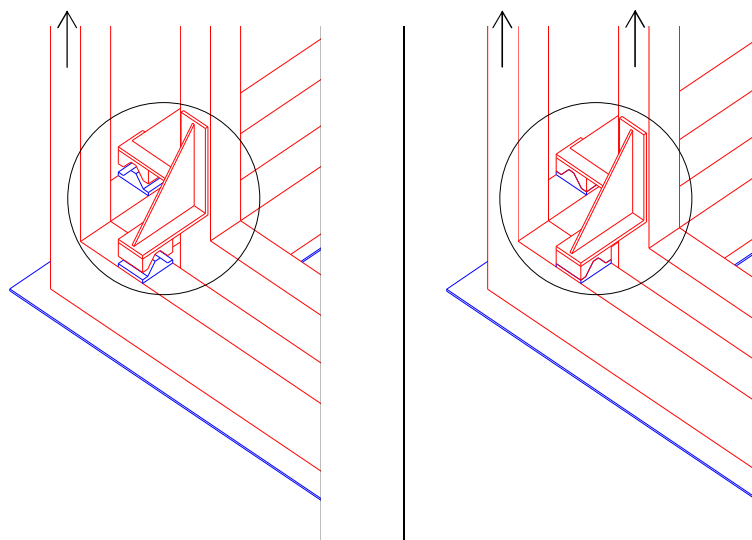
Sistema de encaixe entre as estruturas, exterior e interior da câmara vertical móvel: a) antes da elevação da câmara; b) durante o processo de elevação da câmara.
